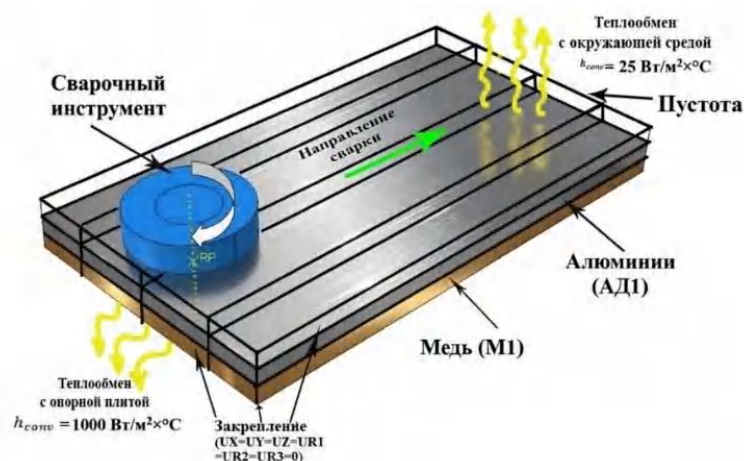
Сборка лагранжевого инструмента и эйлеровой заготовки
